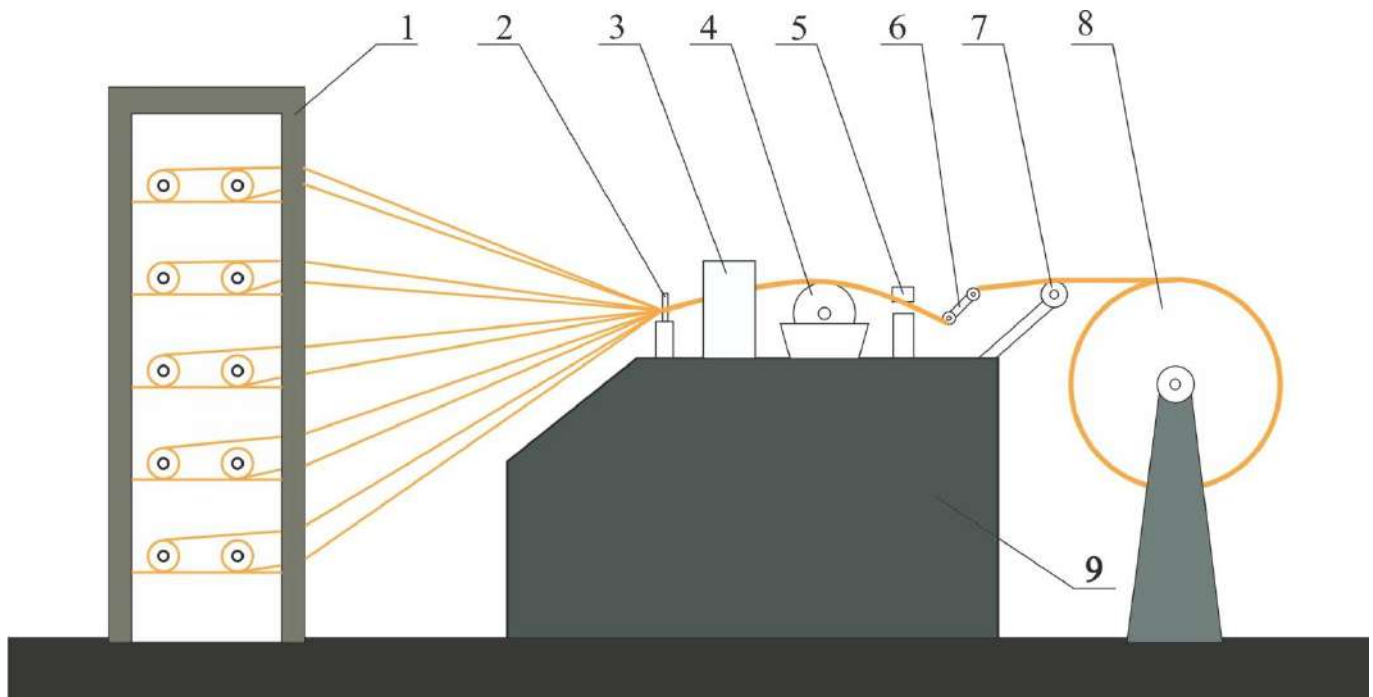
Схема намотки заготовок для бронепанелей и бронещитов: 1 – нитяной шпулярник; 2 – гребенка; 3 – ультрафиолетовая лампа закрытого типа; 4 – пропиточный барабан; 5 – отжимное устройство; 6 – натяжитель; 7 – раскладчик; 8 – оправка; 9 – каретка
